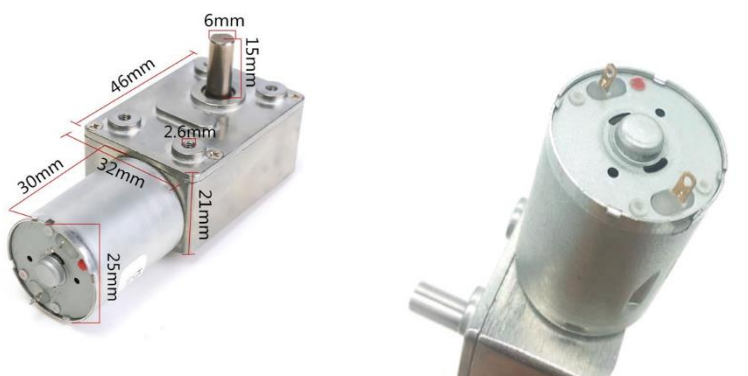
Внешний вид мотор-редуктора JGY-370
